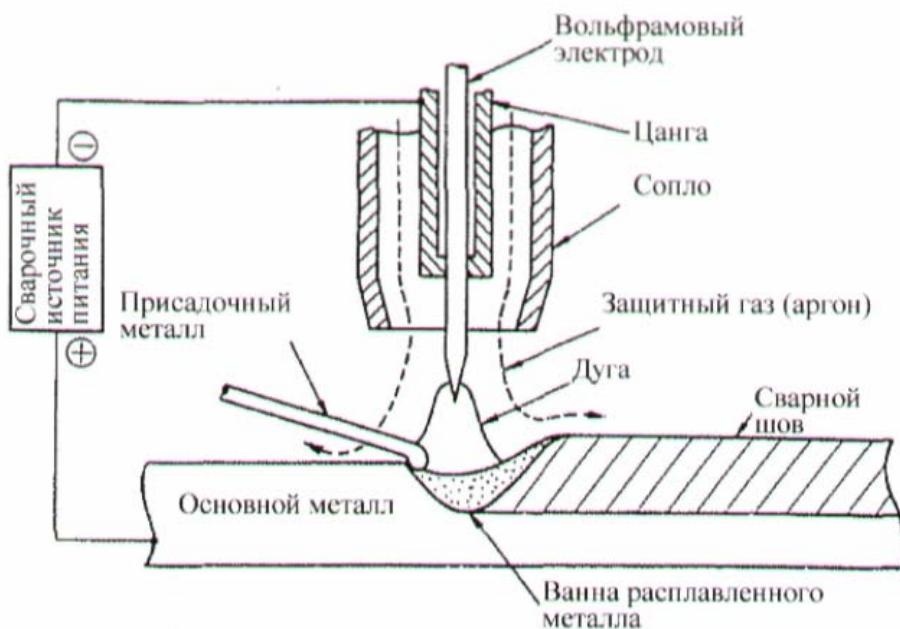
Принцип Аргонодуговой сварки
